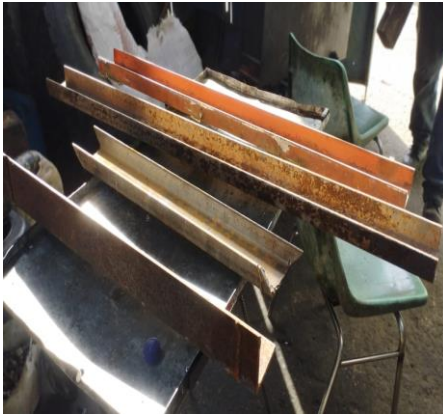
2 vigas en U de 1 metro de largo y 1 viga en U de 1/2 metro. Las tres vigas son de 3 in de ancho y 1/4 in de espesor. 2 vigas en Angulo 1/2 metro de largo, 2 in ancho, 1/4 in grosor, 1 tubo 1/2 metro de largo, 2 3/8 in diámetro exterior.
